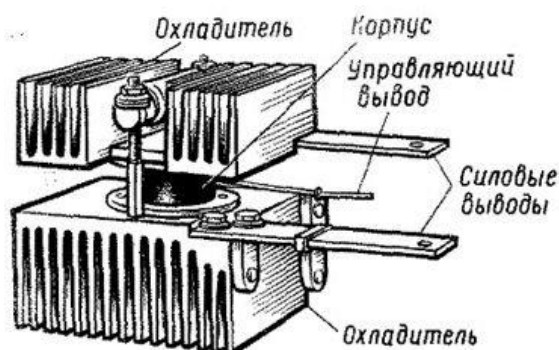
Общий вид тиристора таблеточной конструкции.
